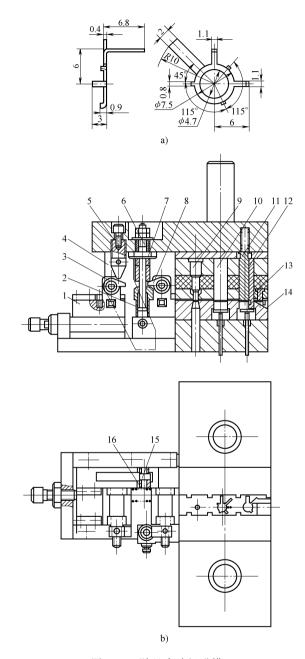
游丝支片级进模 a) 零件图 b) 模具结构图
